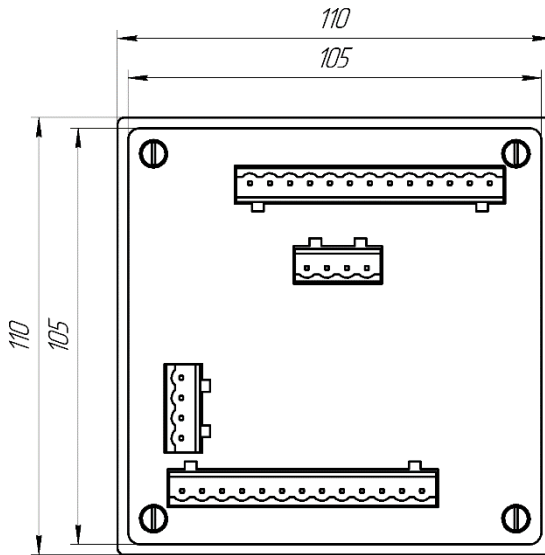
Габаритный чертеж счетчика SM-xAC (вид сзади)
